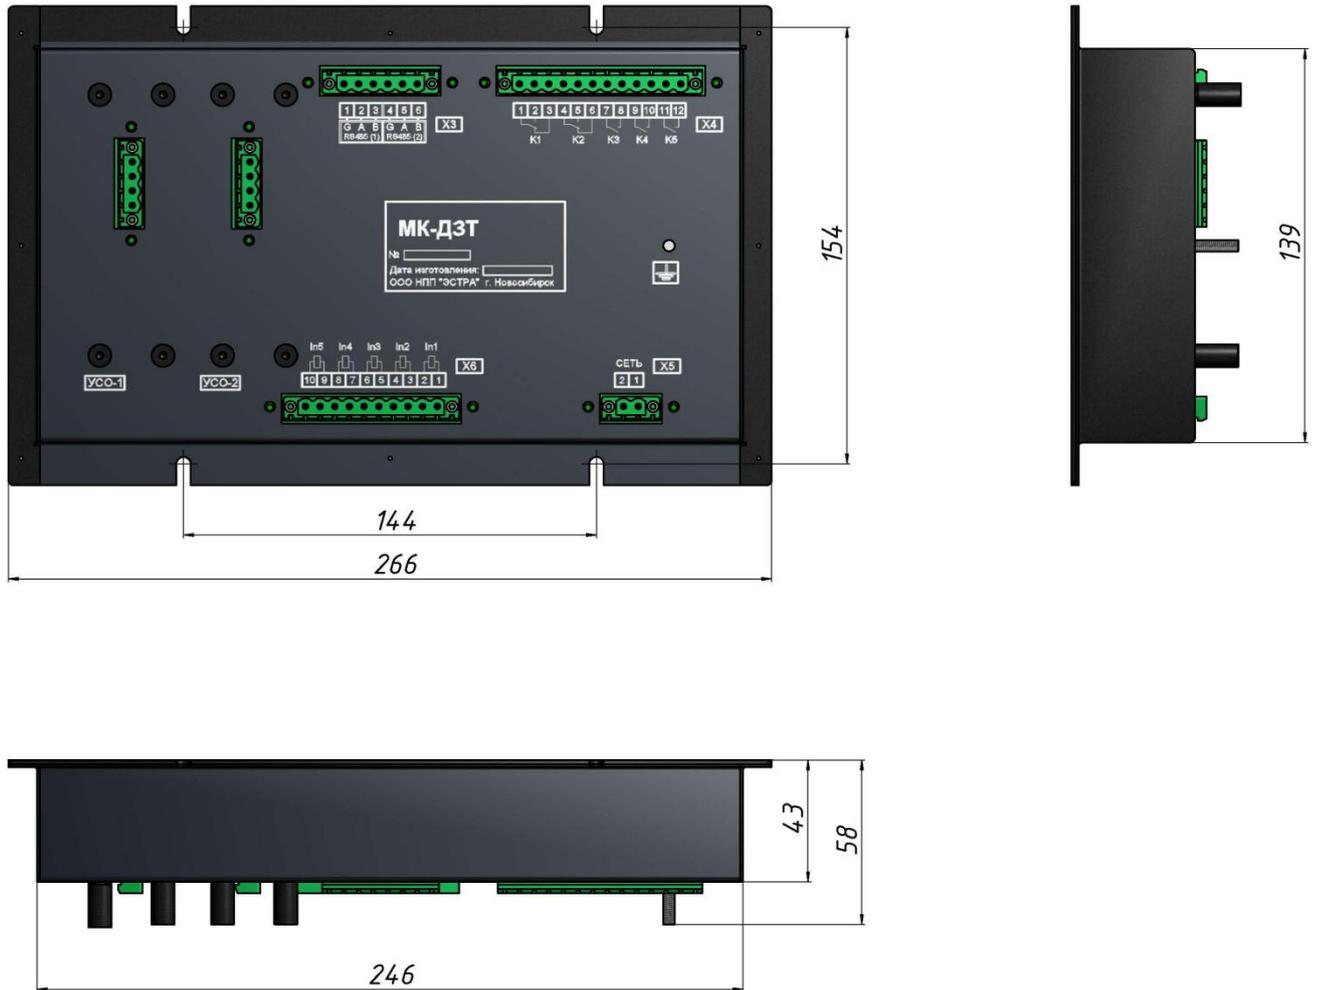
Внешний вид и габаритный чертеж блока защиты
